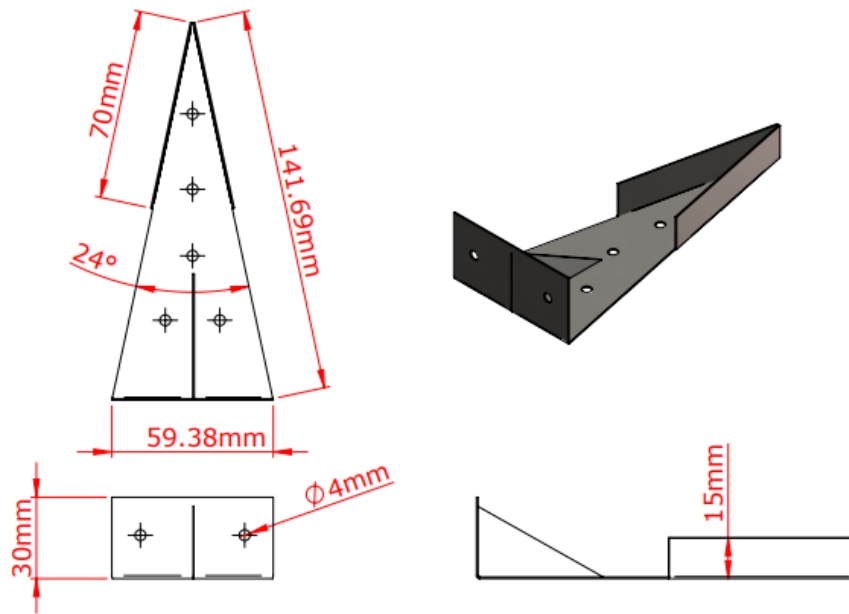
Sección 2 del conducto de extrusión - Detalle de las dimensiones
